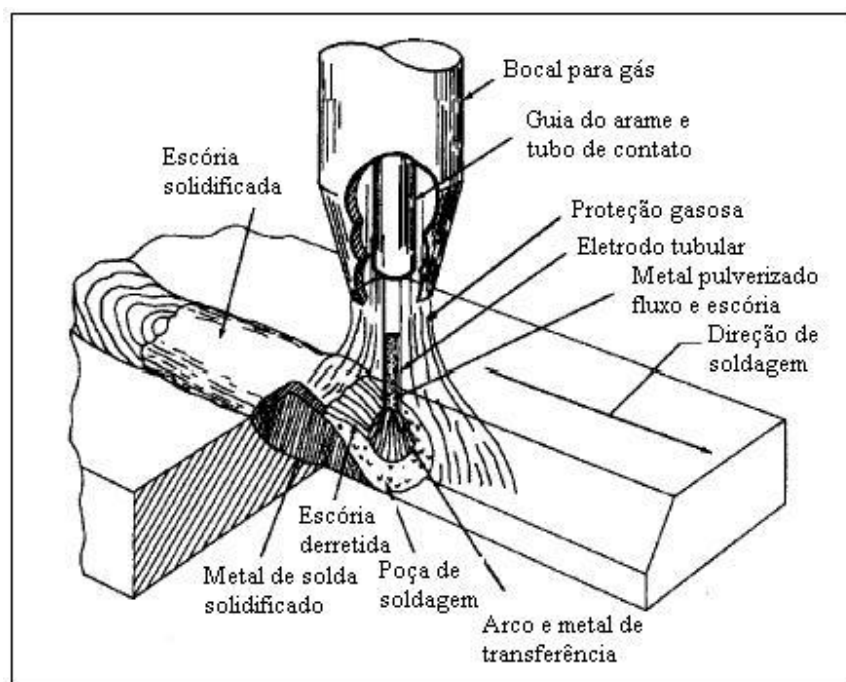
Soldagem com Eletrodo Tubular com proteção gasosa.
